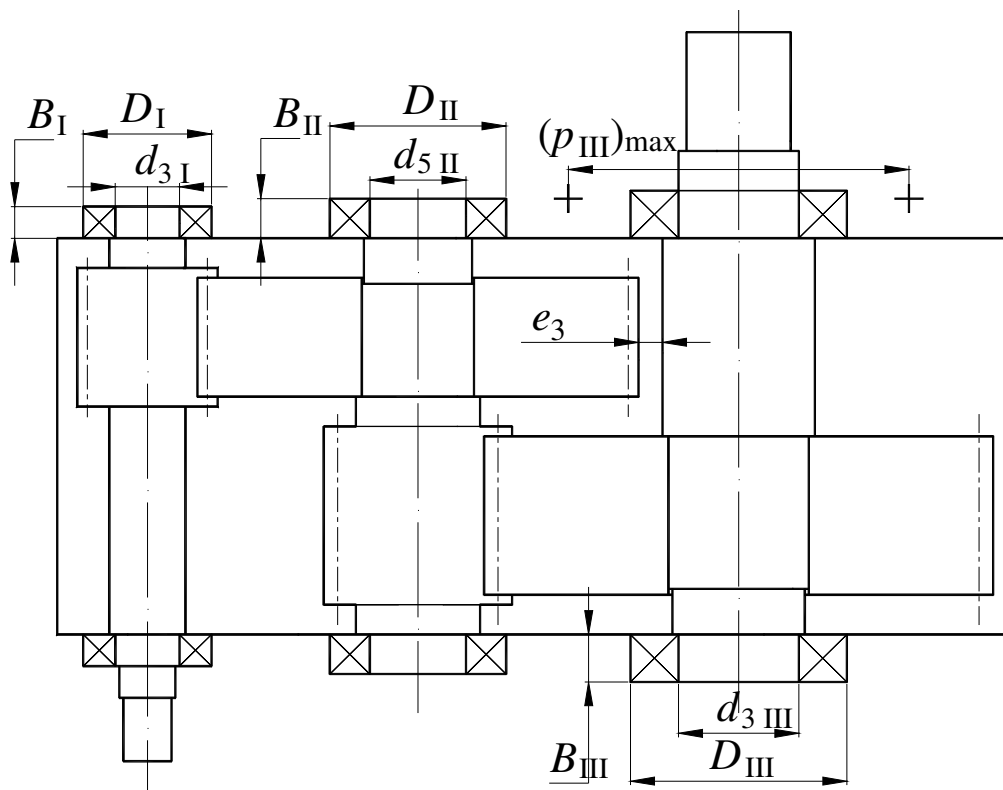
Окончательный результат составления эскизной компоновки цилиндрического редуктора по развернутой схеме
